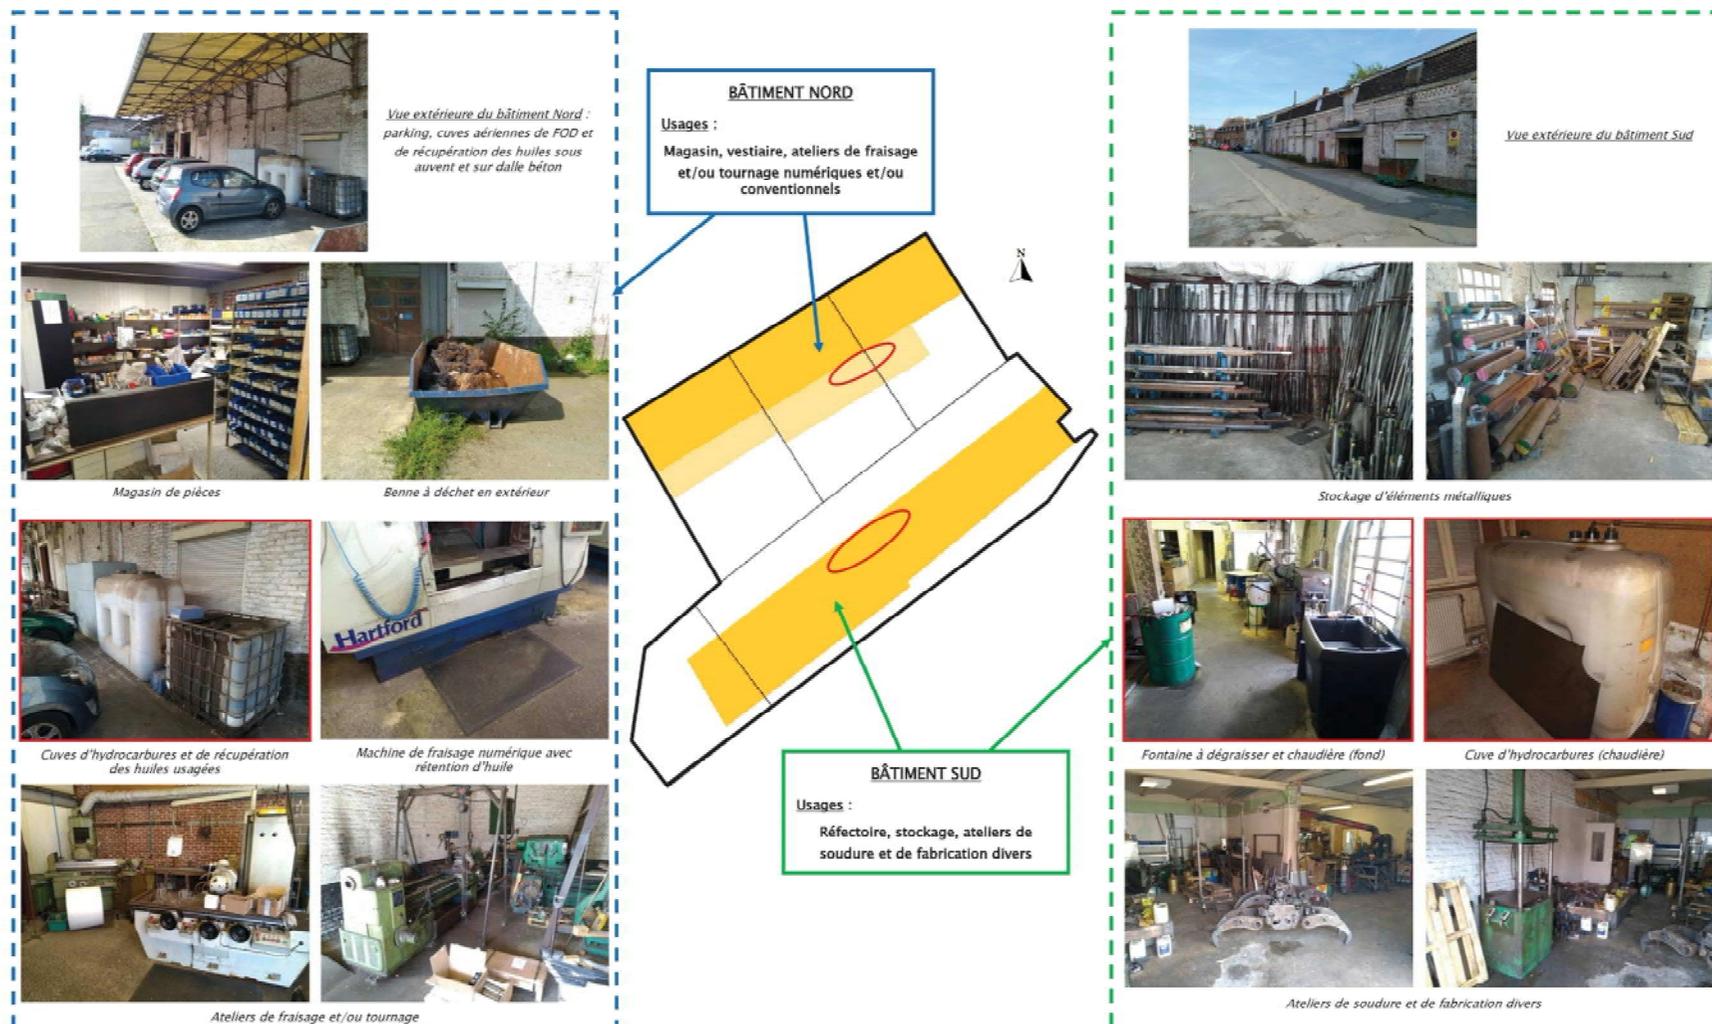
Reportage photographique du site lors de la visite du 21/09/2017
